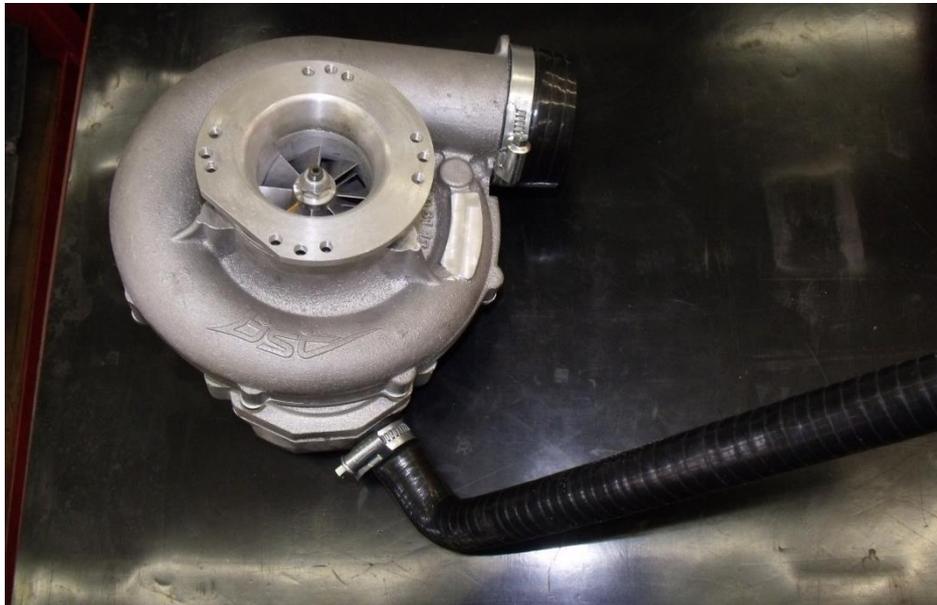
Flanschposition am Kompressor inkl. Verschlauchung
